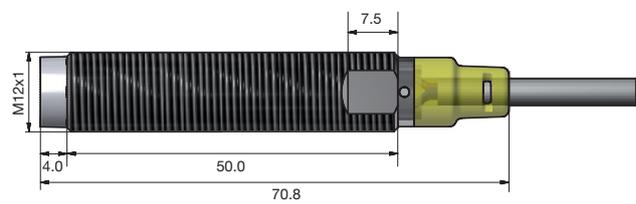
Kurze Ausführung, bündiger Einbau, Steckversion
